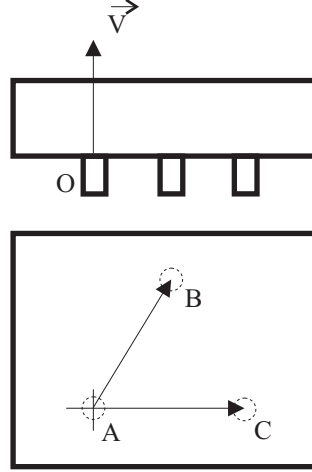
Alzado y perfil de pieza sujeta con 3 apoyos
